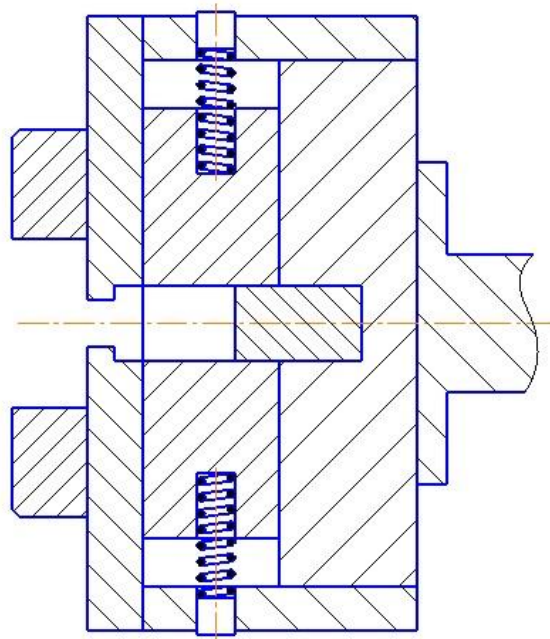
Конструкция барпуллера работающего за счет пружин сжатия.
